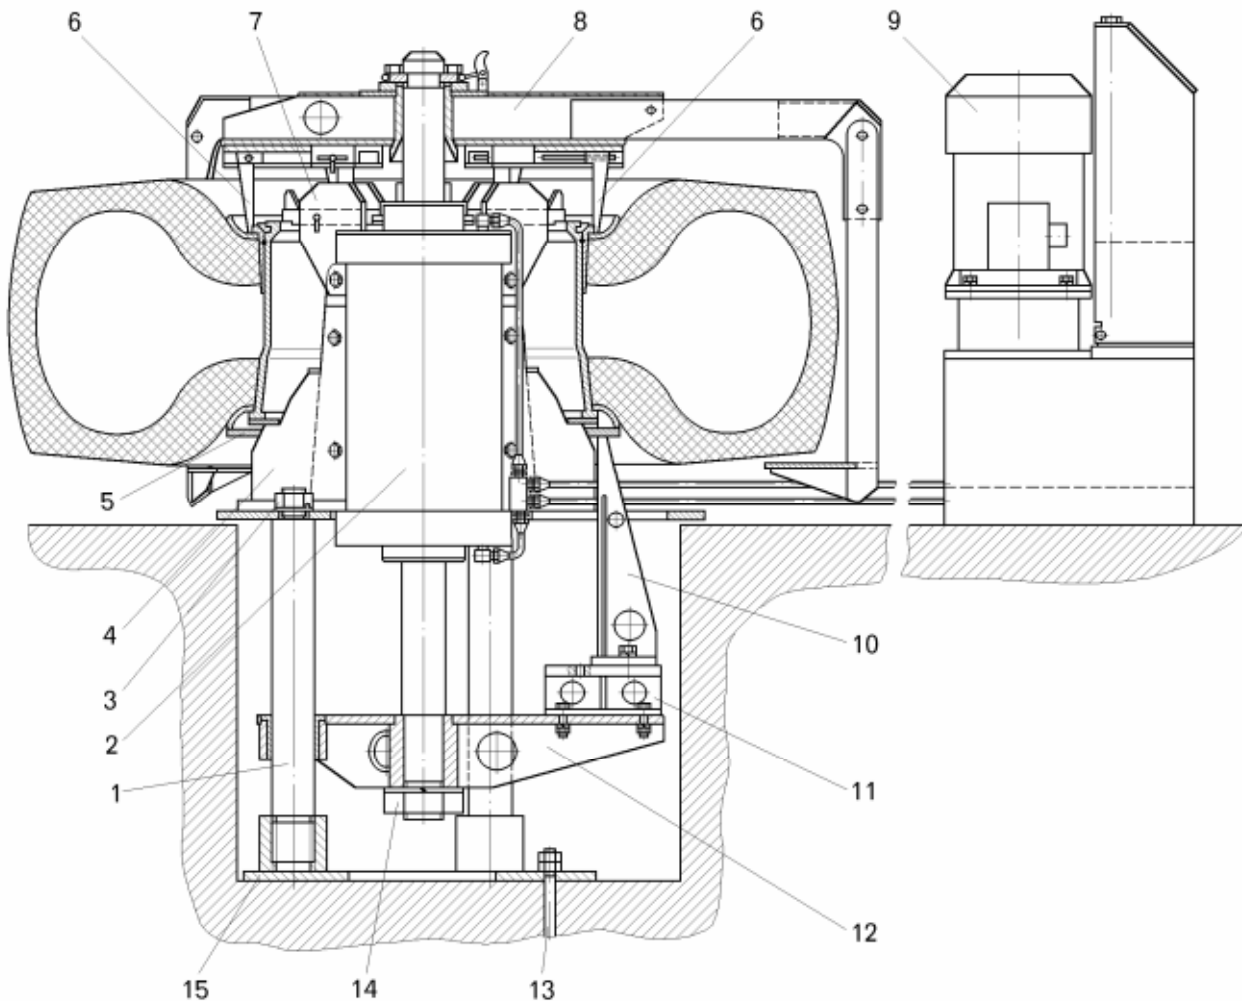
Шиномонтажный стенд для монтажа и демонтажа шин:
